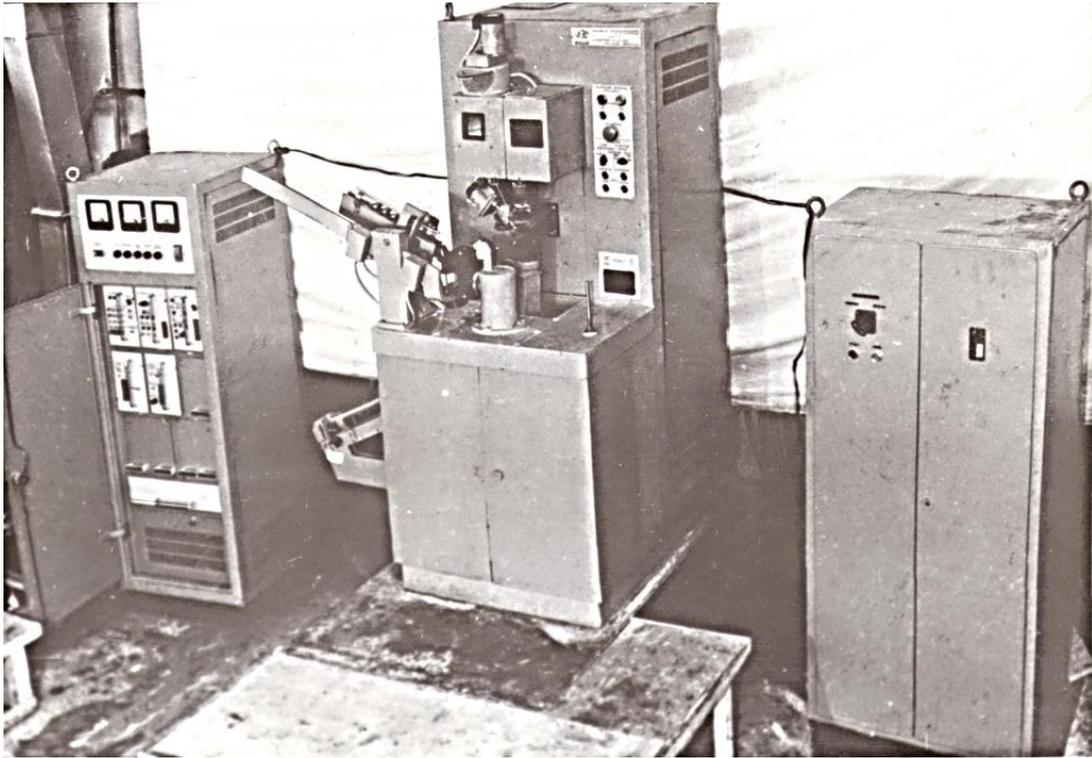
Установка для наплавлення типу ОБІ100
